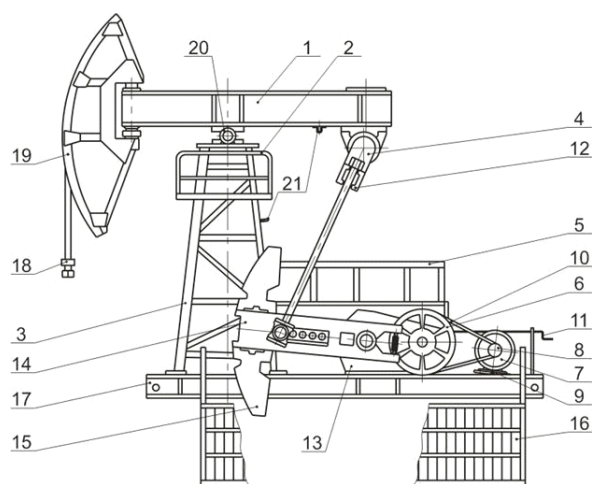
Общая схема конструкции станка-качалки ПШГН8-3-5500
